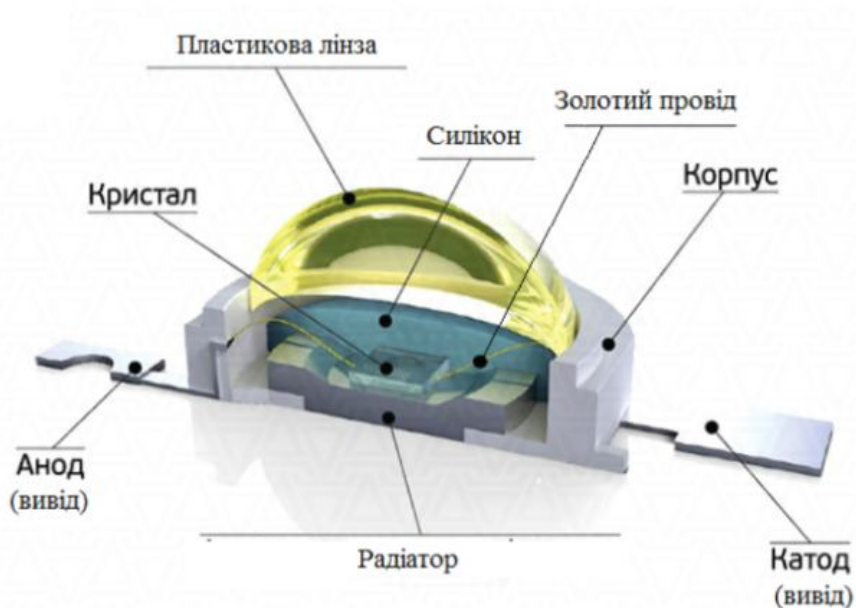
Конструкція SMD-корпуса потужного світлодіода
